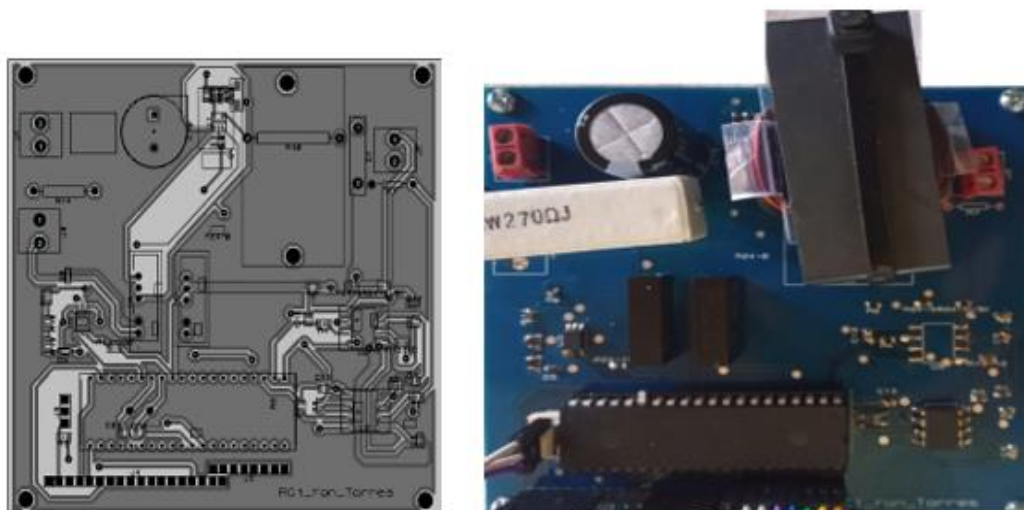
Diseño y montaje de la tarjeta vista superior. (Fuente: autor)
